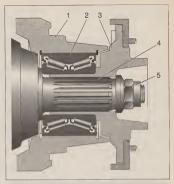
Узел колеса: 1 — поворотный кулак; 2 — подшипник; 3 — ступица; 4 — вал (ось); 5 — гайка.
